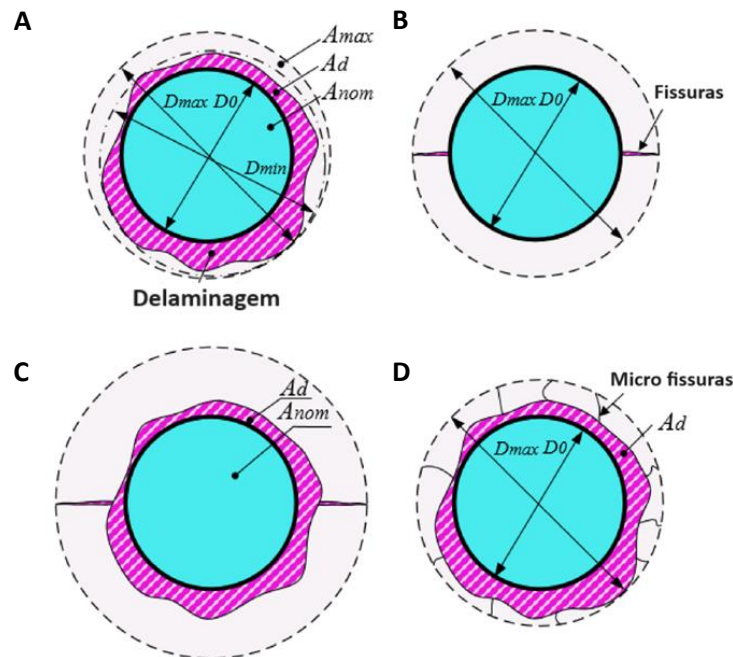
Dano de delaminação: A - dano uniforme, B – fissuras, C - dano com fissuras, D - dano com microfissuras (D); adaptado de [25]
